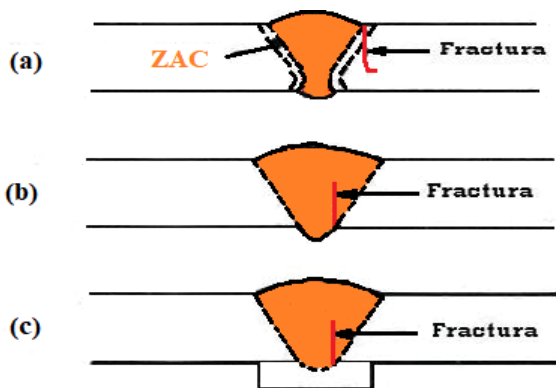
Modos de fractura en soldadura a tope. Fuente: Gurney (1968).
